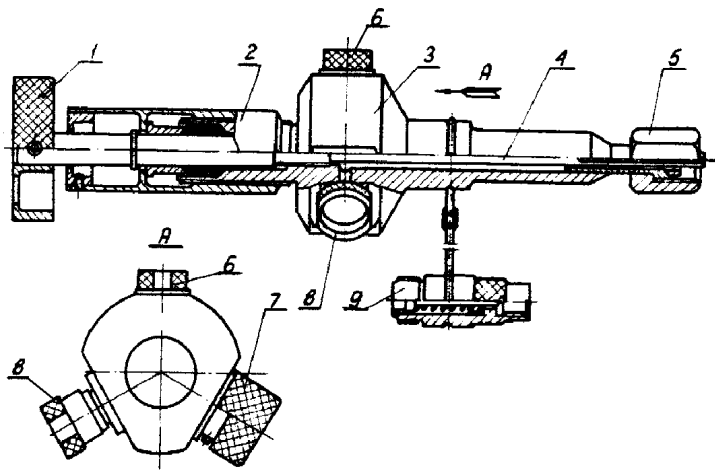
Приспособление $\frac{63740}{028}$ для проверки давления газа в амортизаторах и пневматиках:
